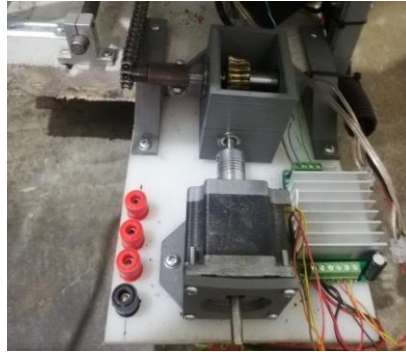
Ensamblaje del motor para el eje X tomado de autor
